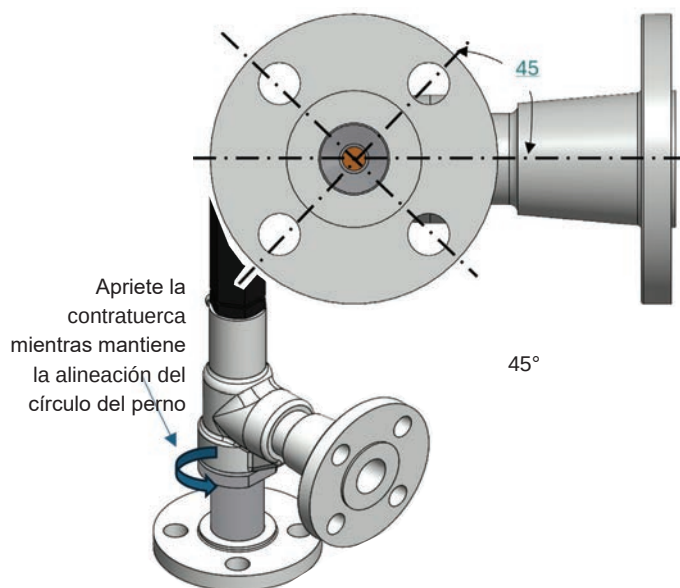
Sincronización de la brida de la contratuerca de soldadura por encastre
